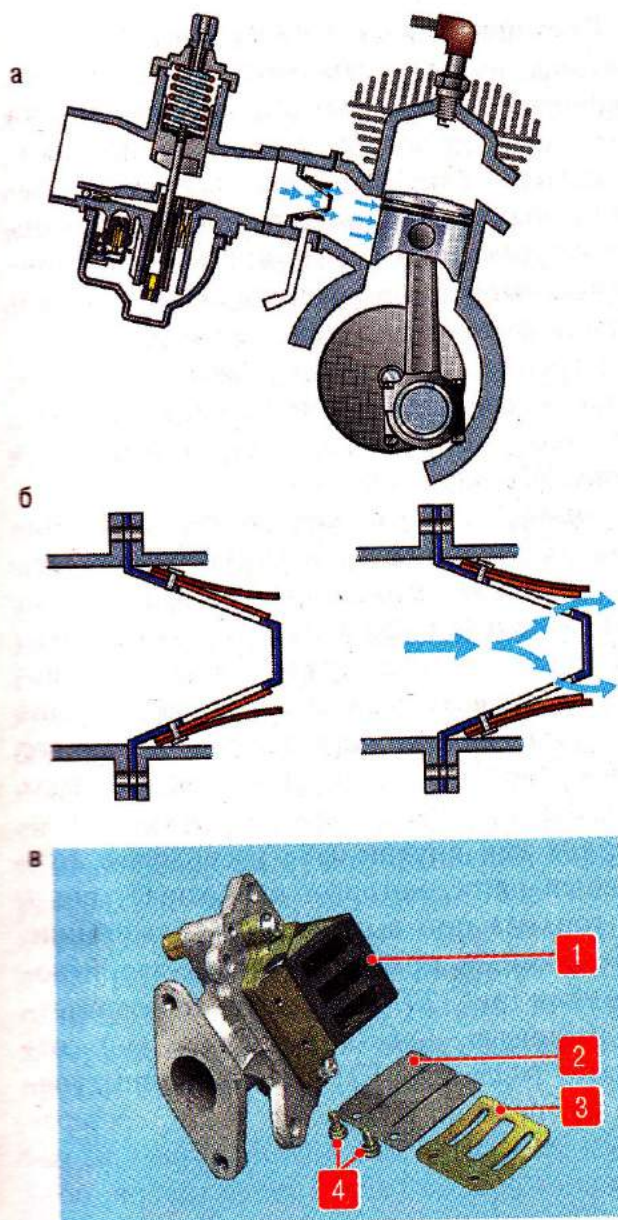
Лепестковый клапан двухтактного двигателя: а – схема размещения; б – принцип работы; в – конструкция; 1 – обрешиненный корпус лепесткового клапана; 2 – упругая пластина; 3 – ограничитель; 4 – крепежные винты
